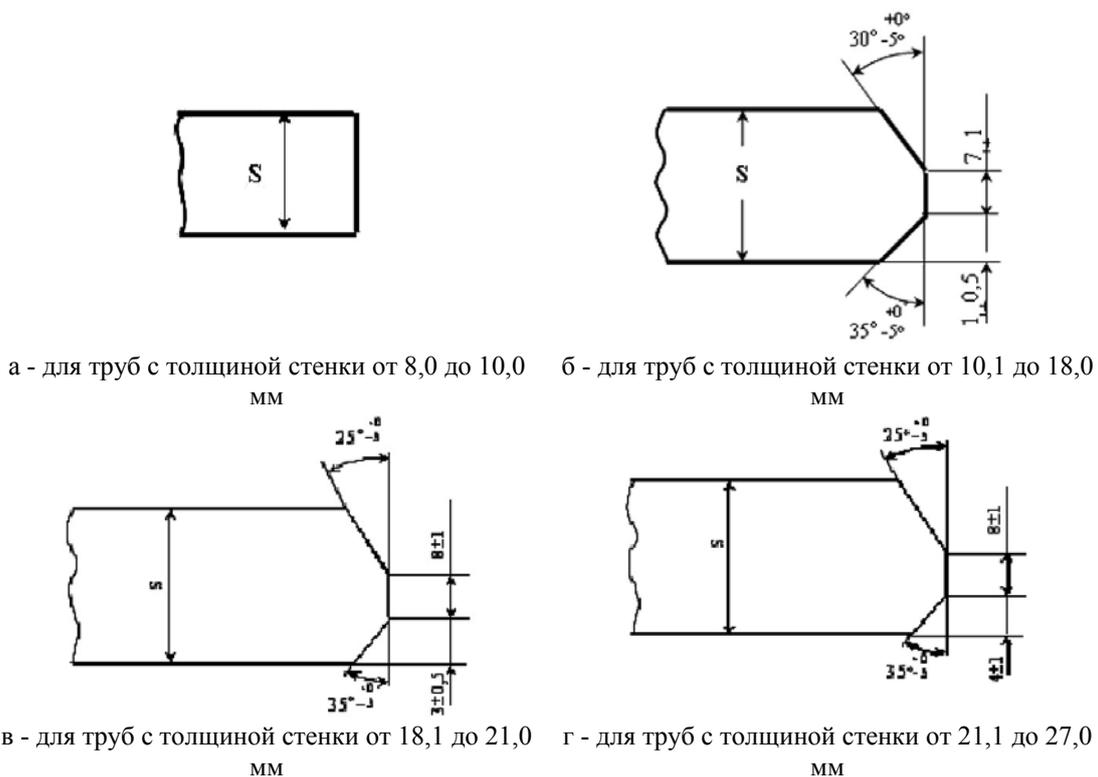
Типы разделки кромок труб диаметром от 1020 до 1220 мм для двусторонней автоматической сварки под флюсом
